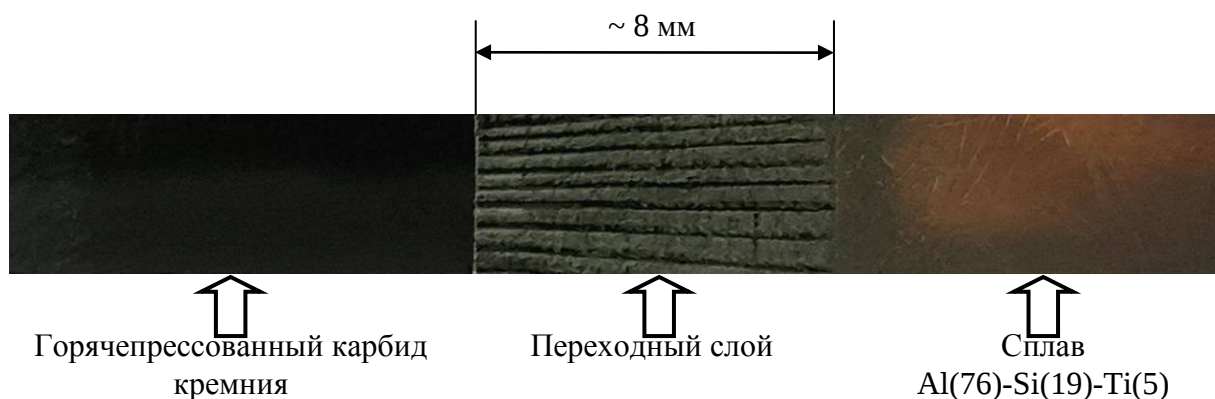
Фотография сварного соединения горячепрессованного карбида кремния с алюминиевым сплавом через переходный слой на основе биоморфного композита.
